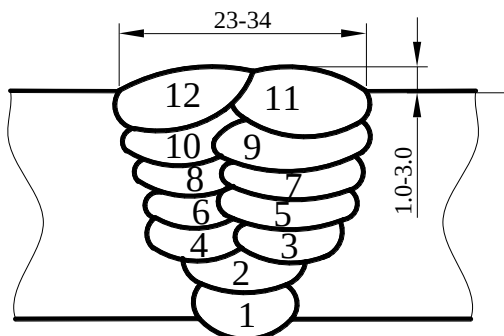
Эскиз сварного шва: мин. кол-во слоев -7, мин. 2 прохода
